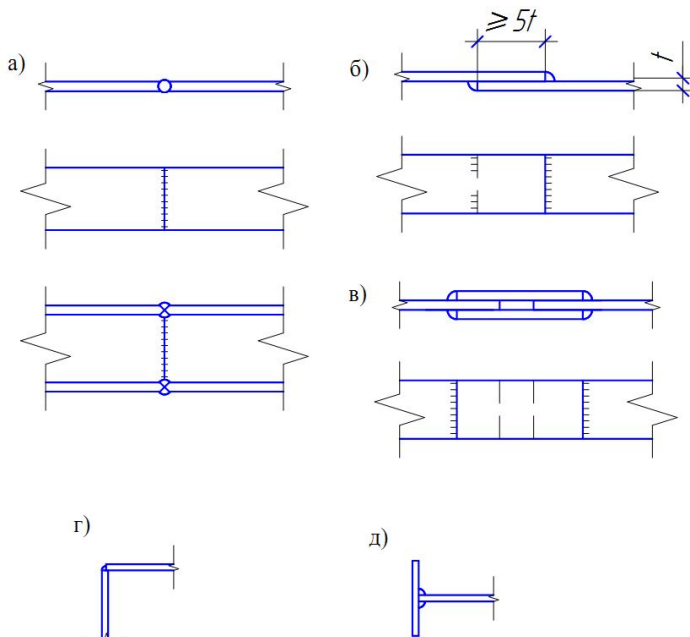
Типи зварних з'єднань: а – стикове; б – напусткове; в – з накладками; г – кутове; д – таврове
